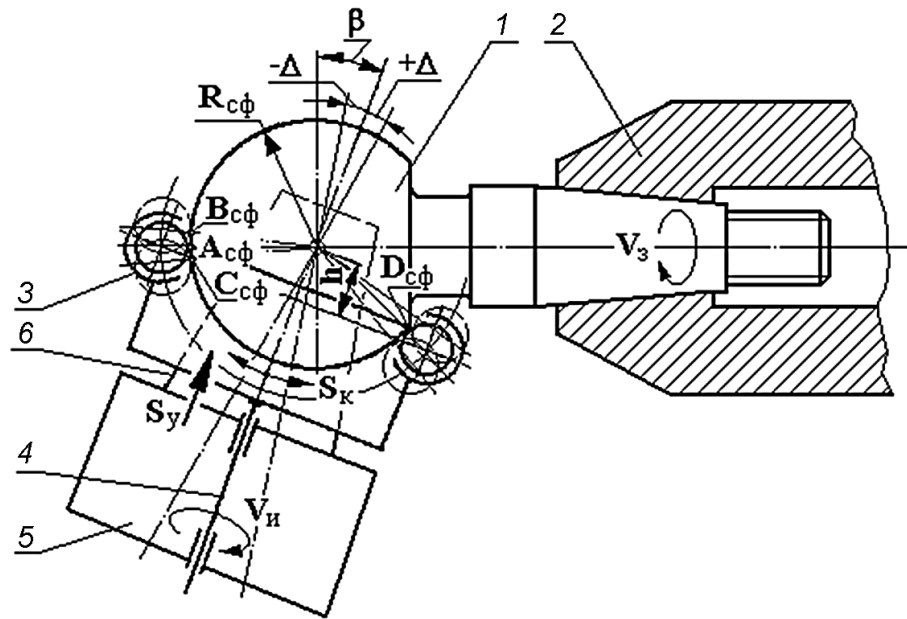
Схема обкатки бессепараторным инструментом.
